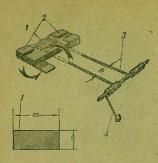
Якорь пишущего реле: I—жестяные пластинки якоря, 2—обоймы, скрепляющие пластинки якоря, 3— шарнир якоря, 4—хвостовой крючок шарнира.
